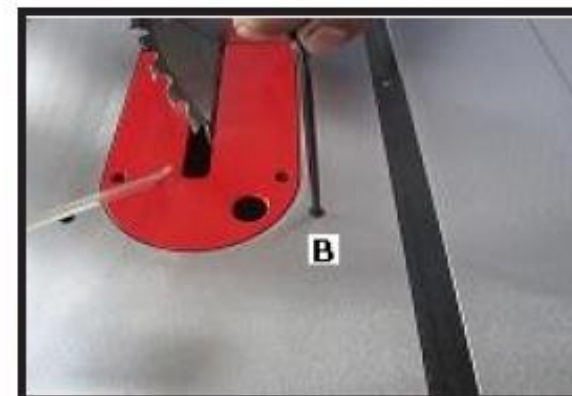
Регулировка положения под углом 45° с помощью установочного винта
